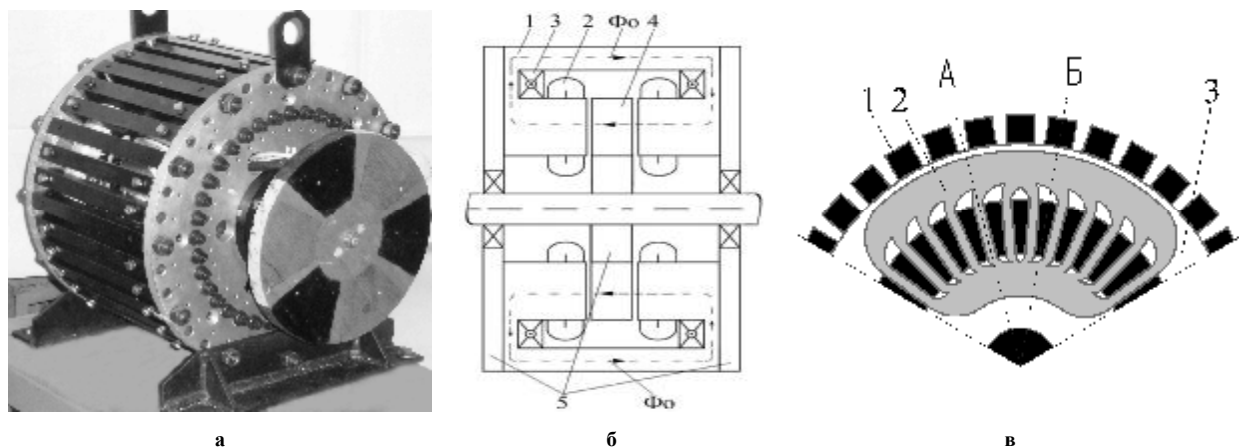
Торцевой двигатель постоянного тока индукторного типа:
